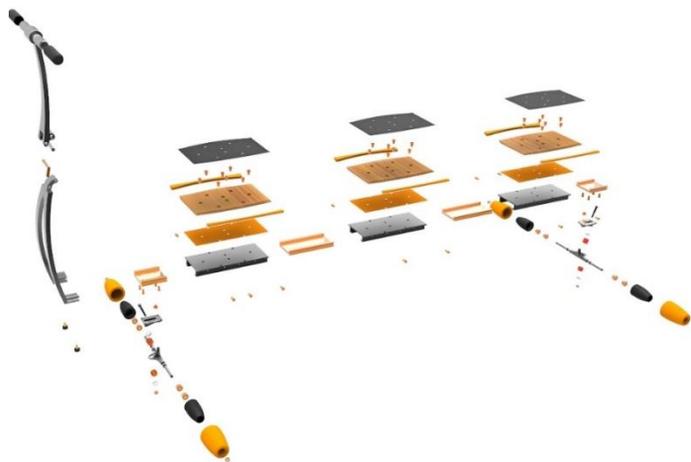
Ejemplo Planos de Armado. (Sandro Proyectos)
